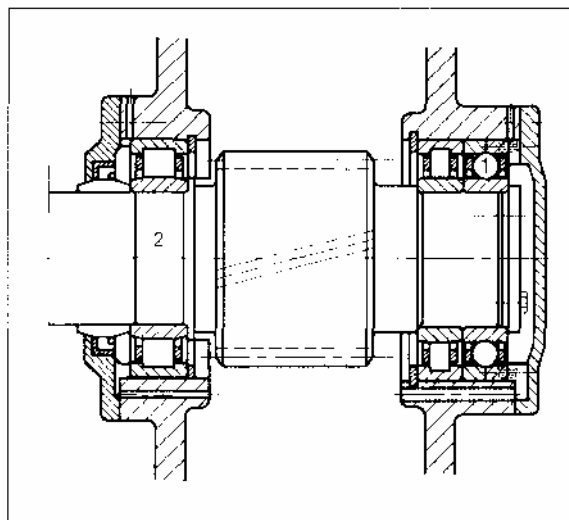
Palier fixe par roulement à 4 points de contact (doc. SKF).
